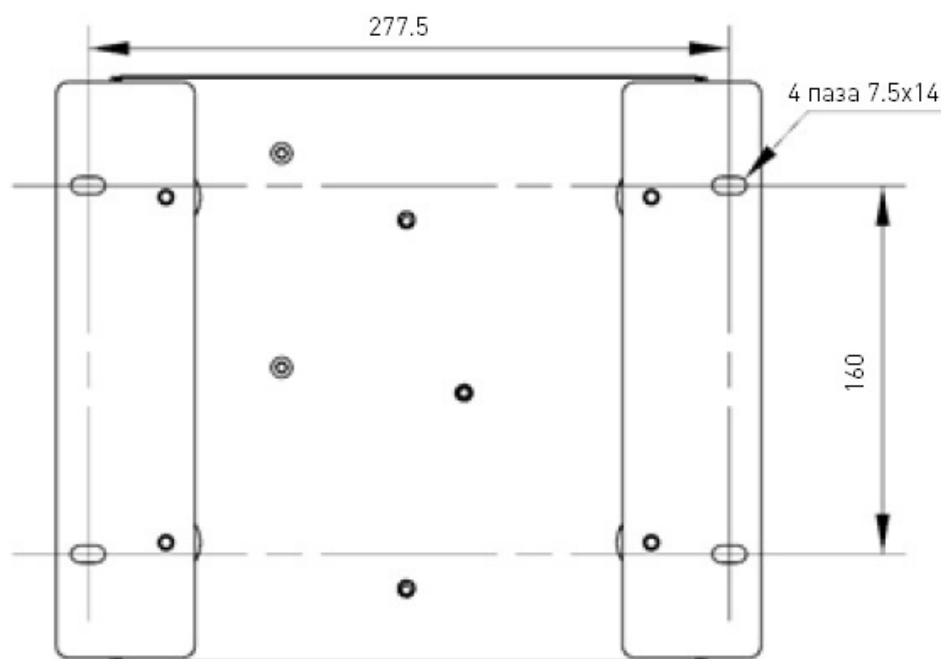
Размеры для установки ВЧ-блока поджига.
